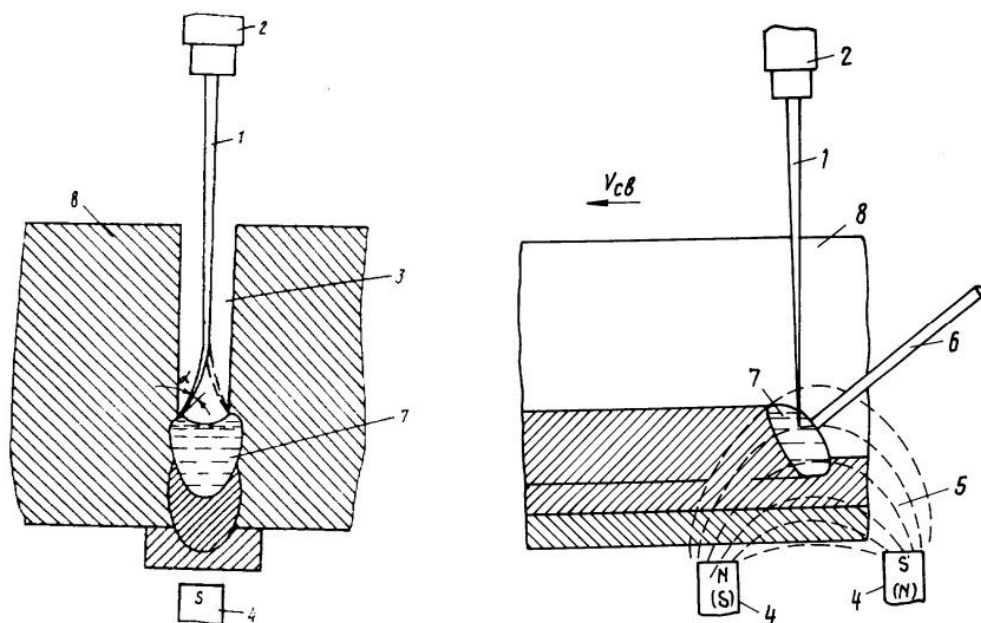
Схема способа многослойной ЭЛС с присадочной проволокой: 1 – луч; 2 – излучатель; 3 – зазор; 4 – магнитная система; 5 – линии поля; 6 – присадочная проволока; 7 – сварочная ванна.
